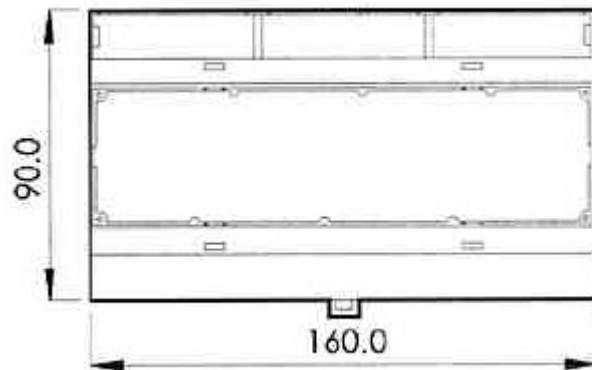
Przykładowy widok wnętrza centrali modularPAG®.
